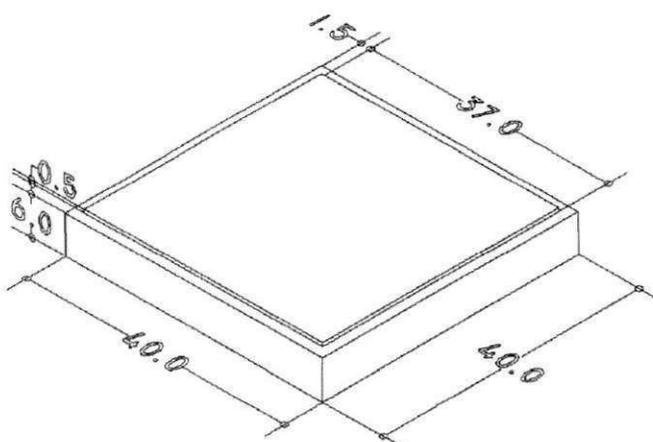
Dimensão do bloco de EPS (medidas em mm).
